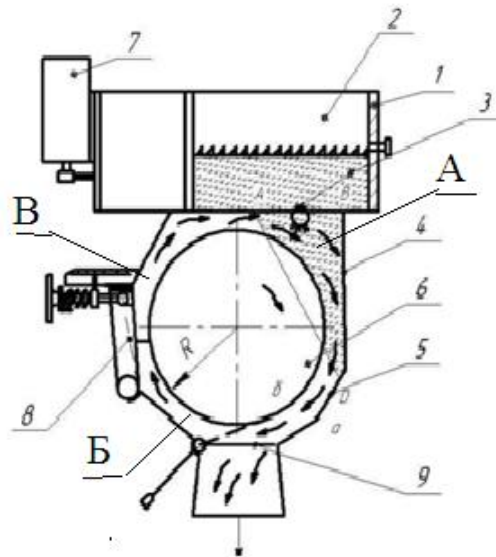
Принцип побудови й роботи дискретної безлопатевої тістомісильної машини (ДБТМ): 1. вібратор борошна; 2. ємність для борошна; 3. нагнітальний пристрій рідких компонентів; 4.місильна камера; 5. дільниця зважувального змішування; 6. місильний барабан; 7. електродвигун постійного струму; 8. пасивний вібраційний пристрій (пластифікатор); 9. шибєр вивантаження тіста
